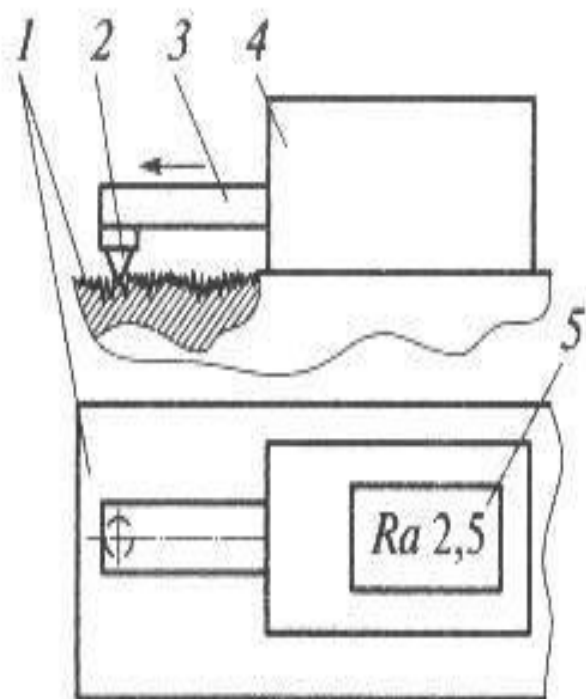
Измерение шероховатости поверхности с помощью малогабаритного накладного профилометра:
